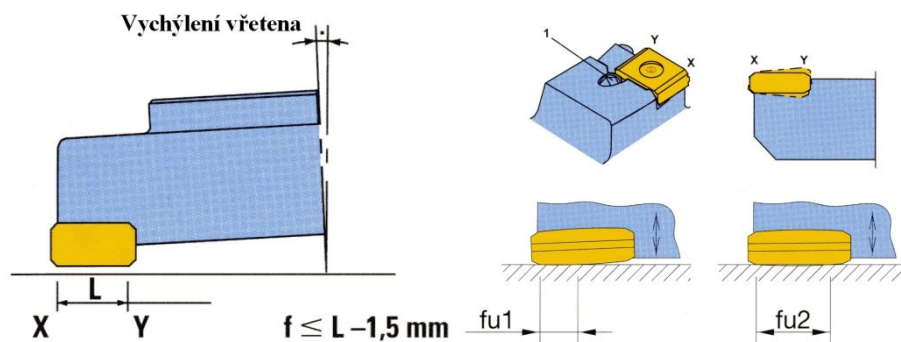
Porovnání standardních VBD a VBD s wiper geometrií [49]
